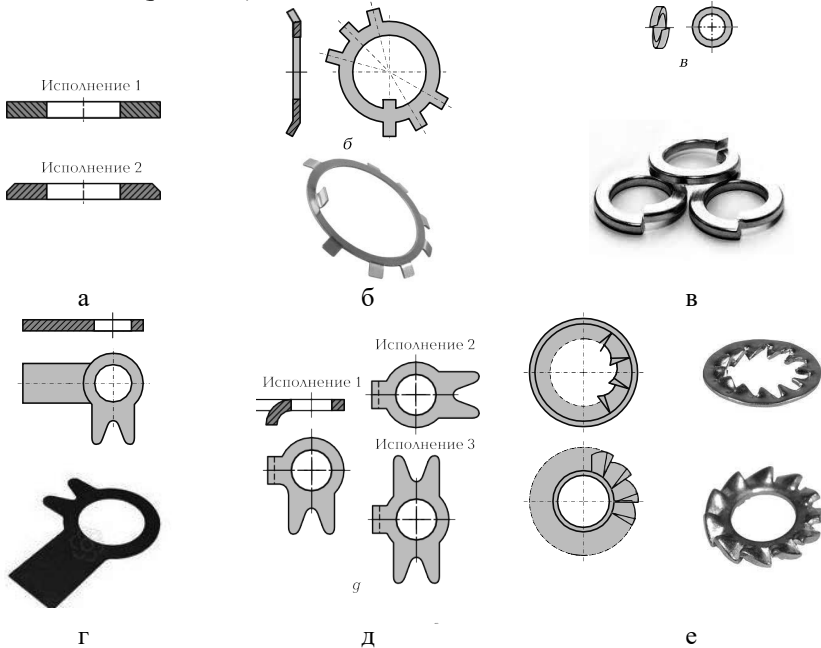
Шайби: а – звичайна плоска; б – стопорна багатолапчата; в – пружинна; г – стопорна з лапками; д – стопорна з носком; е – стопорна із зовнішніми і внутрішніми зубами
